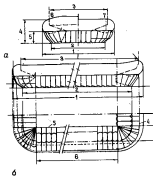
Композиционная схема ГО американского КВЛ JEFFA: а - вид сверху и сбоку; 1 - ширина судна наибольшая; 2 - ширина ВП; 3 - ширина жесткого корпуса; 4 - возвышение верхней точки крепления гибкого ресивера к жесткому корпусу; 5 - высота ГО; 6 - над с носом; 7 - над с кормой; б - вид сверху и снизу; 1 - длина судна наибольшая; 2 - длина ВП; 3 - длина жесткого корпуса; 4 - линия присоединения НЗ к гибкому ресиверу; 5 - внутренняя линия присоединения бортовых НЗ к жесткому корпусу; 6 - длина участка стандартных бортовых НЗ
